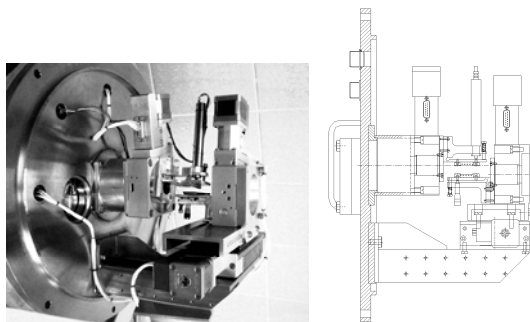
Внешний вид монохроматора и его сборочный чертеж.
